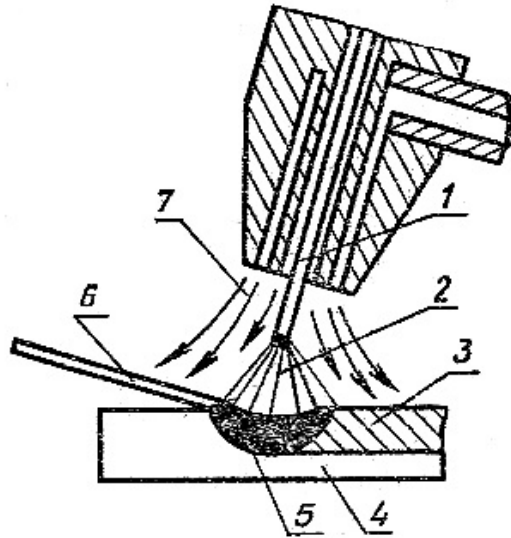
Аргонно-дугове наплавлення: 1-електрод, 2-дуга, 3-наплавлений метал, 4-основний метал, 5-ванна розплаву, 6-присадний дріт, 7-аргон.
